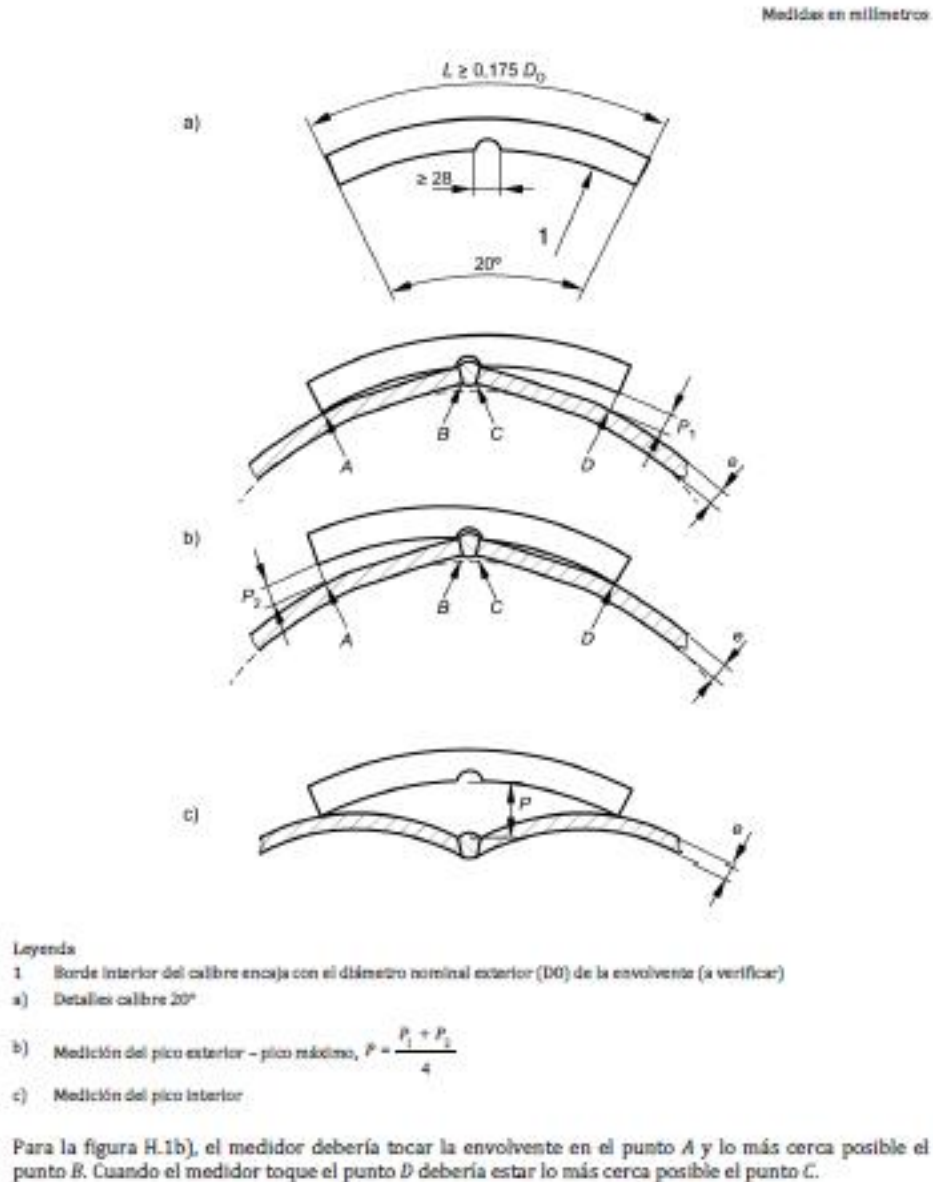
Esquema construcción medidor de picos de la envolvente. UNE-EN 12493
